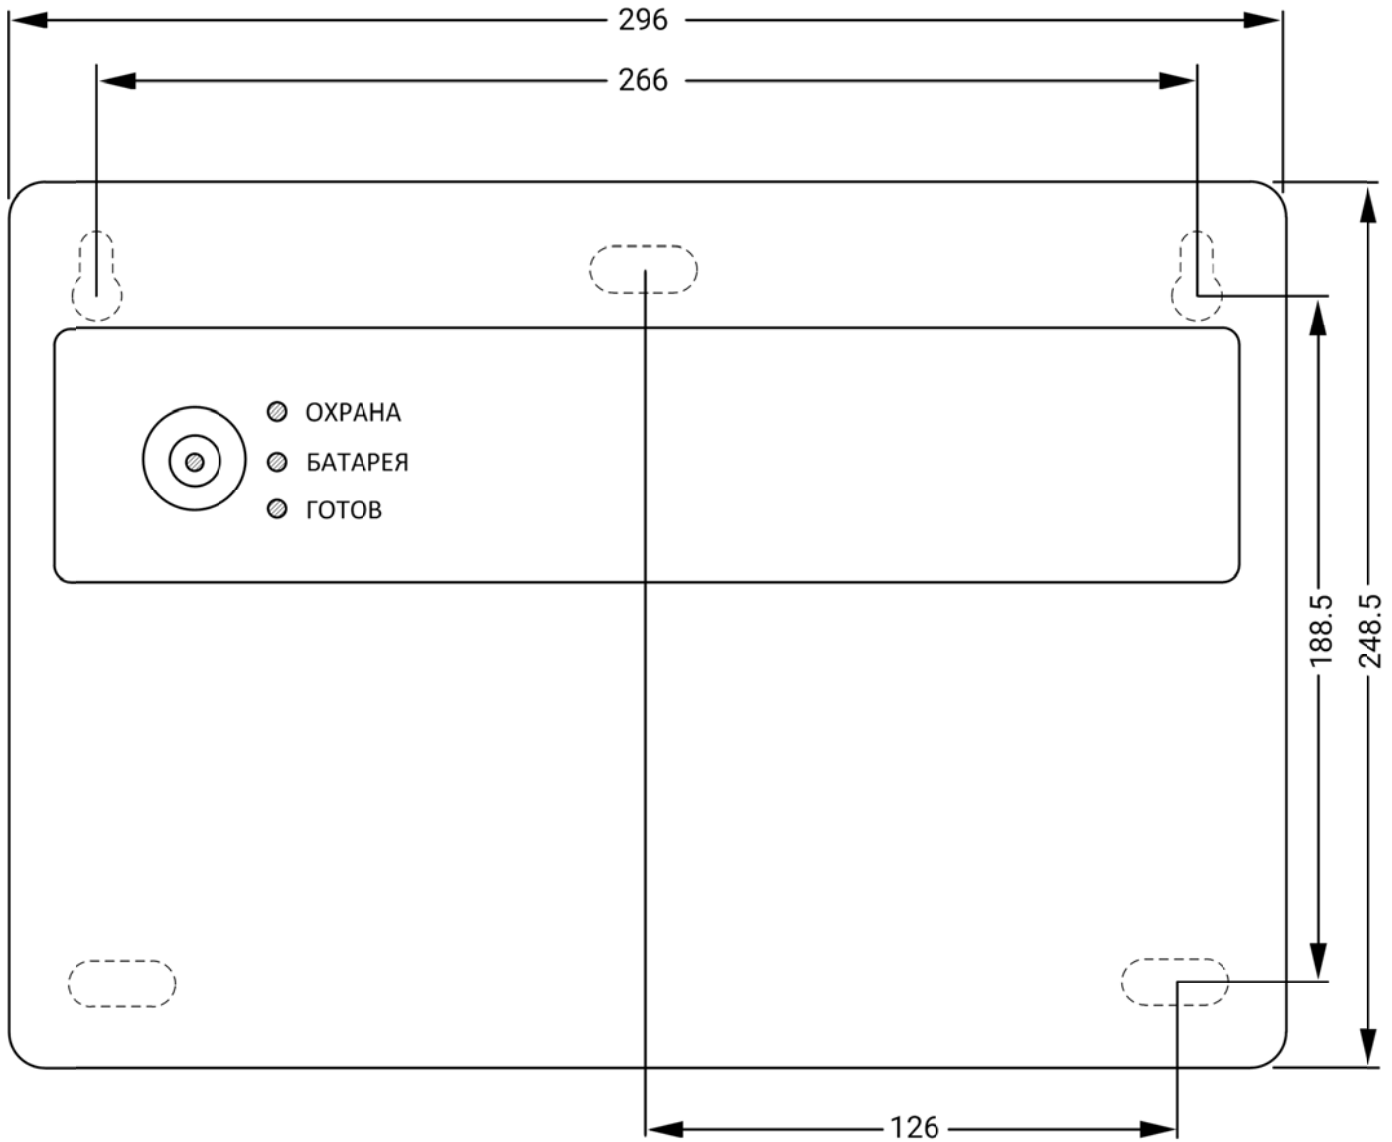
Корпус «Контакт» под АКБ 7 Ач³
